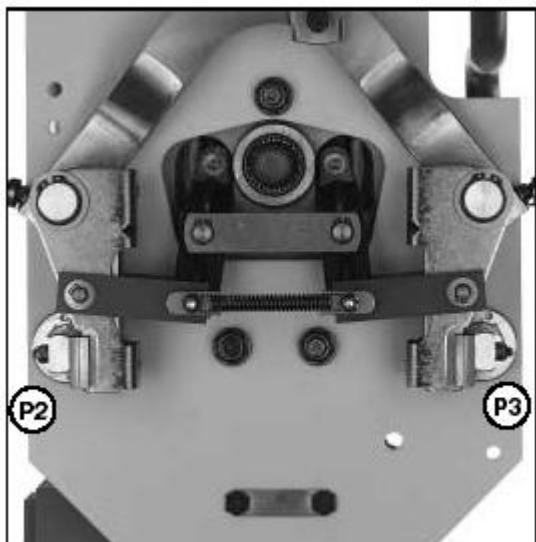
Однофазный шунтирующий переключатель, расположение шин P2 и P3
